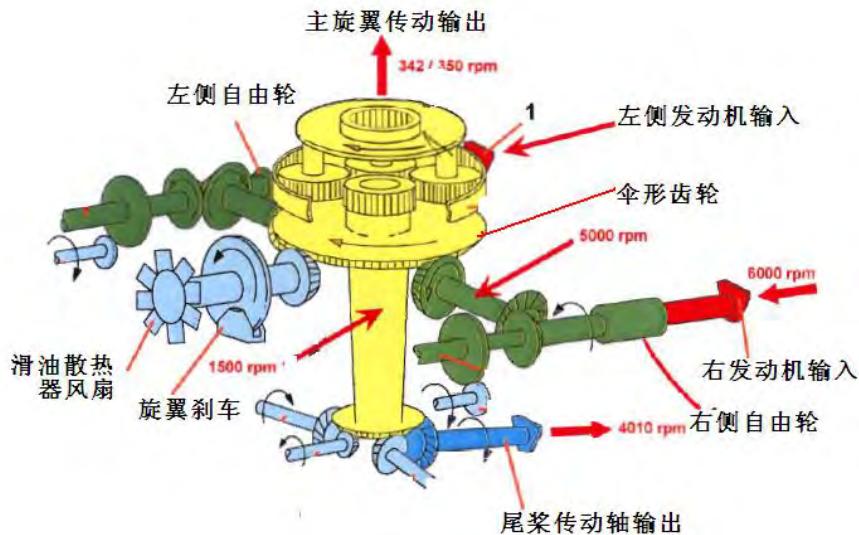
典型主减速器内部齿轮及轴系传动方式示意图
